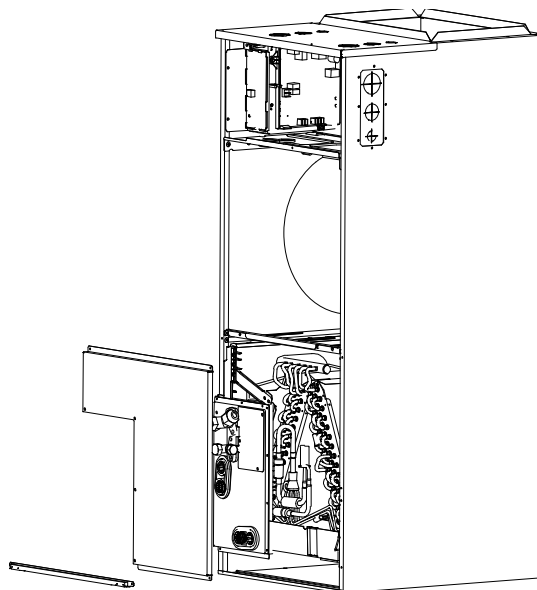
Retirez la plaque du couvercle de l'évaporateur
